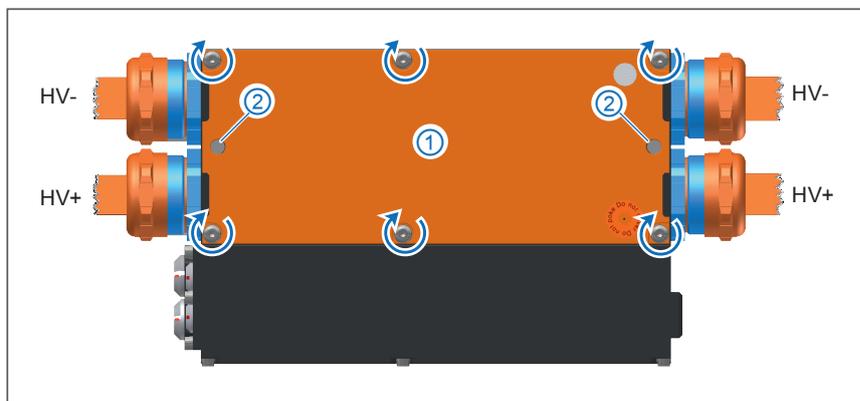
HV BM 1.2, HV-Leitungen montiert, Gehäuse geschlossen
